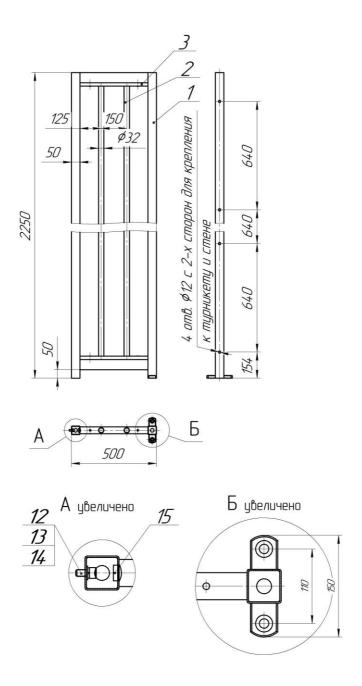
Конструкция, габаритные и установочные размеры ограждения ОПР/500
